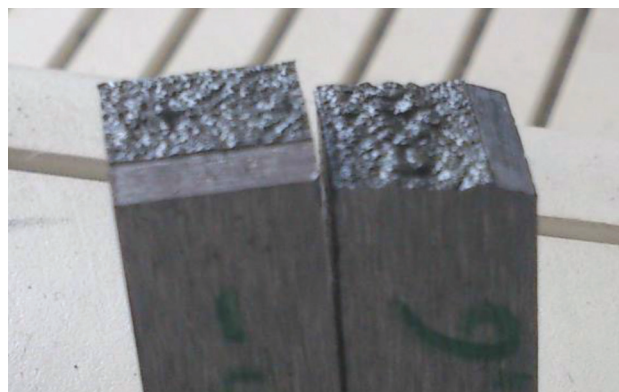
Superficie de fractura ASTM A36 a -44°C.
